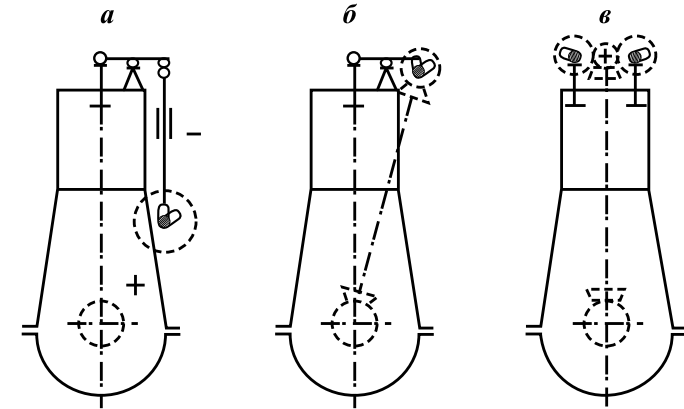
Схеми механізмів газорозподілу з верхнім розміщенням клапанів з передачею зусилля від розподільного вала на клапани: а – через штовхач, штангу і коромисло; б, в – через конічні шестерні при верхньому розташуванні розподільного вала
